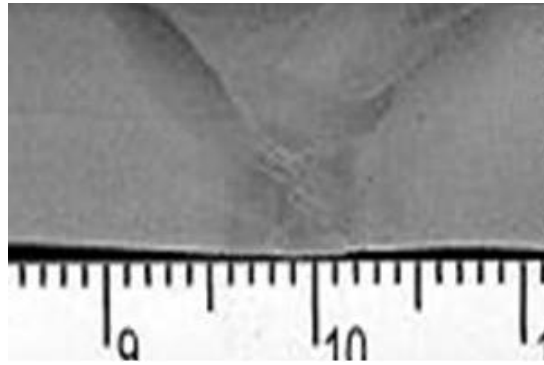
Macrografia da chapa de teste, passe de raiz soldado com GMAW e os demais com FCAW.
